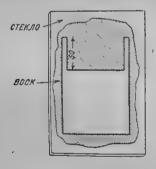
Заготовка формы для отливки аккумуляторной пластины.
